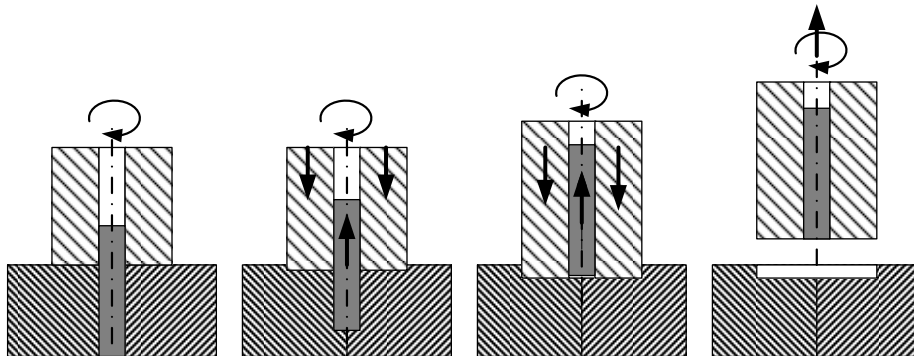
Retractable Pin Tool (Werkzeug bewegt sich nicht in Vorschubrichtung)
